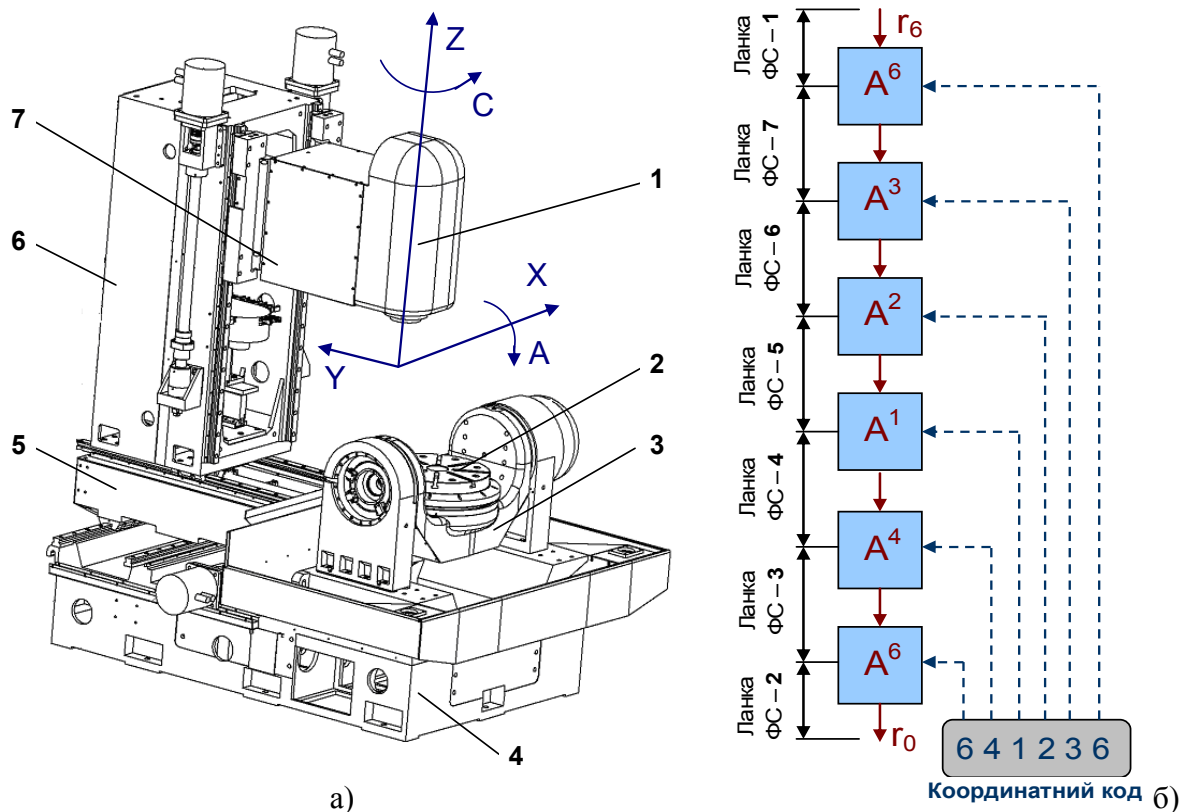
Основні вузли (а) та формуюча структура п'ятикоординатного фрезерного верстата з ЧПК: 1 – шпиндель; 2 – вертикальний поворотний стіл; 3 – горизонтальний поворотний стіл; 4 – основа; 5 – поперечний стіл; 6 – рухома стійка; 7 – шпиндельна бабка
